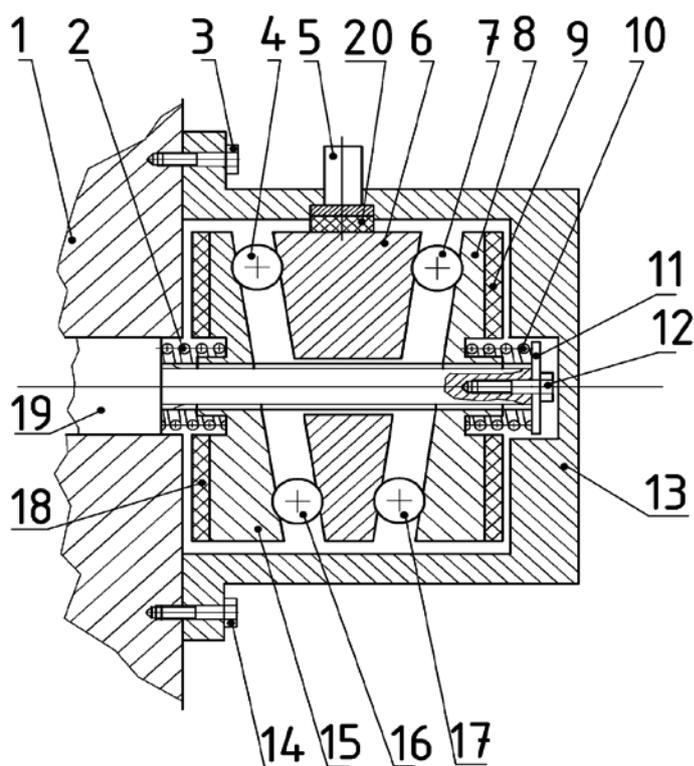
Тормозной механизм: 1 – корпус заднего моста; 2 – возвратная пружина левая; 3 – винт крепления крышки; 4 – шарики; 5 – шток; 6 – промежуточный диск; 7 – корпус тормоза; 8 – ведущая шестерня конечной передачи; 9 – фрикционная накладка; 10 – возвратная пружина правая; 11 – упорная шайба; 12 – винт крепления шайбы; 13 – кожух; 14 – винт крепления крышки; 15 – нажимной диск; 16 – шарик; 17 – шарик; 18 – фрикционная накладка; 19 – шлицевой вал; 20 – фрикционная накладка
